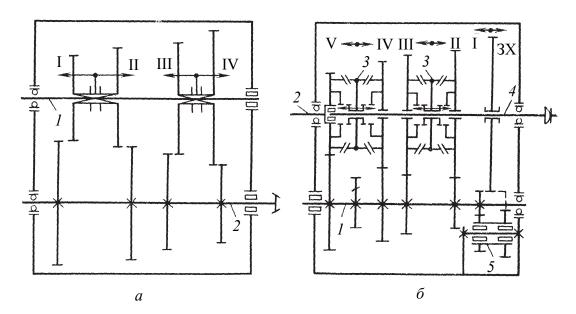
Схемы коробок передач: a — тракторная двухвальная: I — ведущий вал; 2 — ведомый вал; δ — автомобильная: I — промежуточный вал; 2 — ведущий (первичный) вал; 3 — синхронизаторы; 4 — ведомый (вторичный) вал; 5 — блок шестерен реверса; I—V — номер передачи; 3X — задний ход
